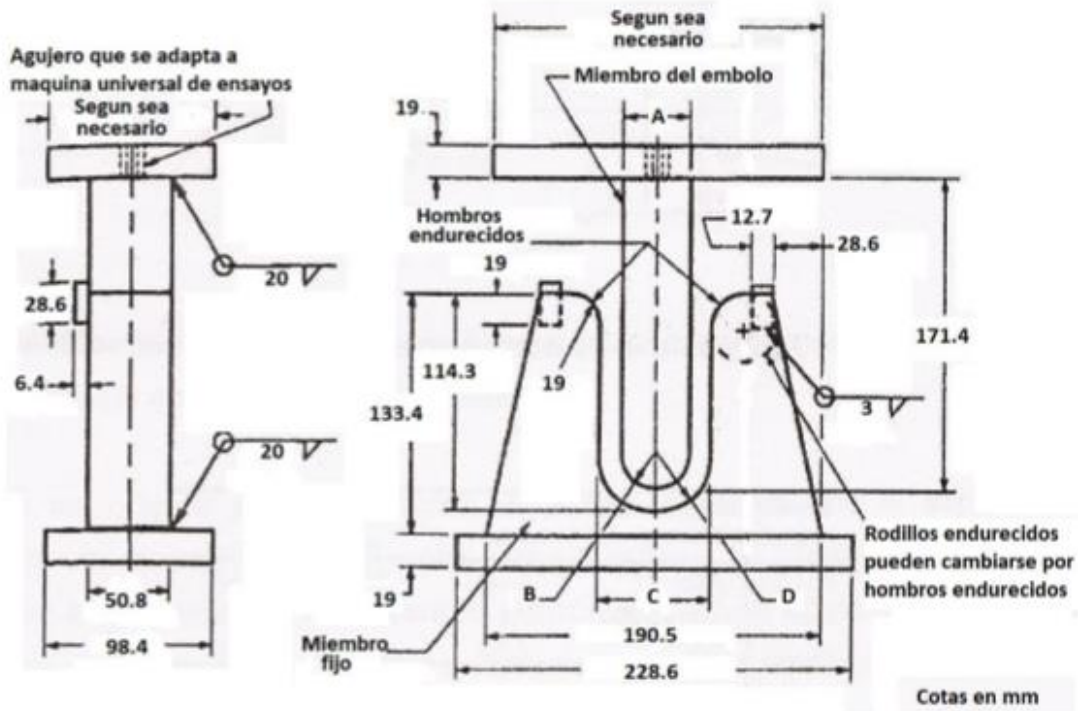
Utillaje utilizado para en ensayo doblado guiado [21]
